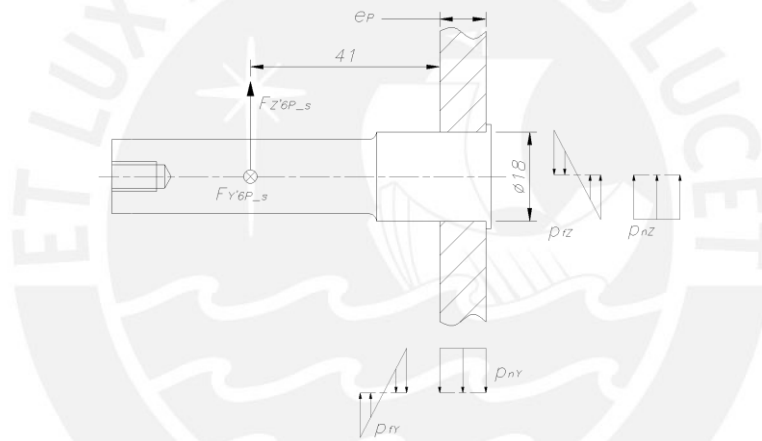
Presiones de aplastamiento en zona de apoyo.
